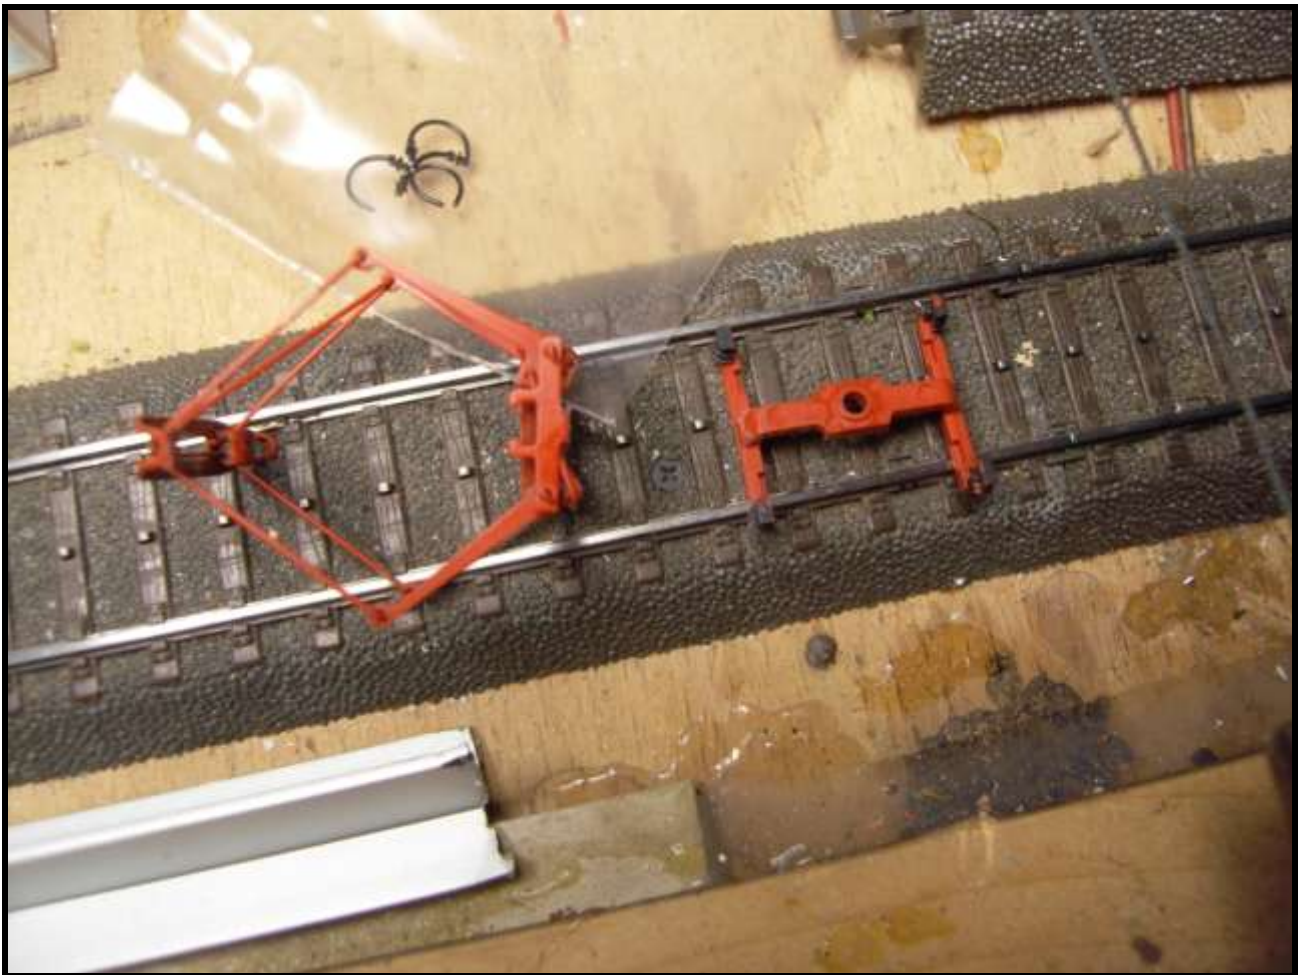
si separa la base dall'archetto fissata a pressione.
